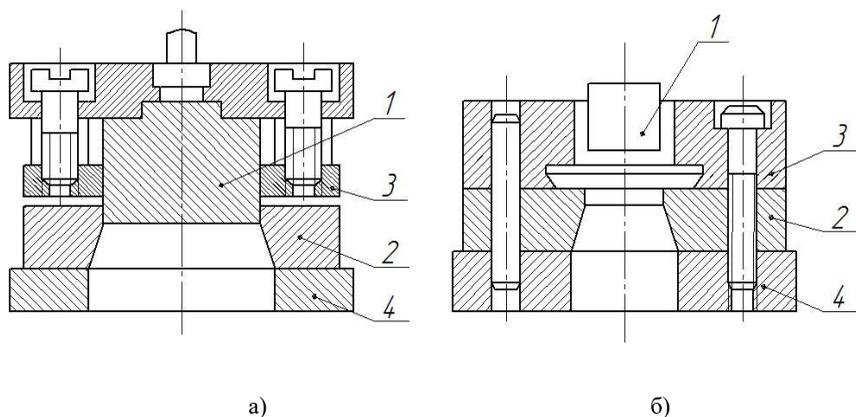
Конструкции съемников: а – подвижный; б – жесткий;
